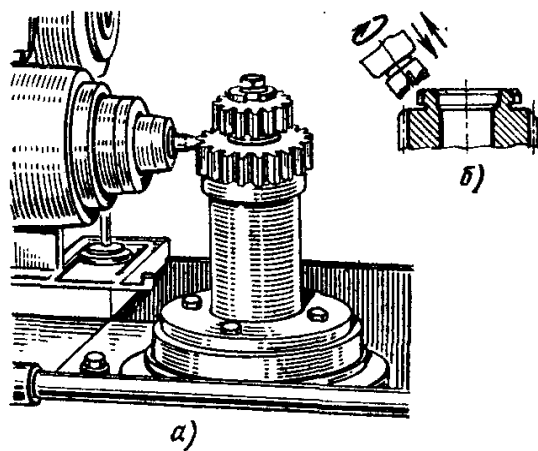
Схеми заокруглення зубів циліндричних зубчастих коліс
